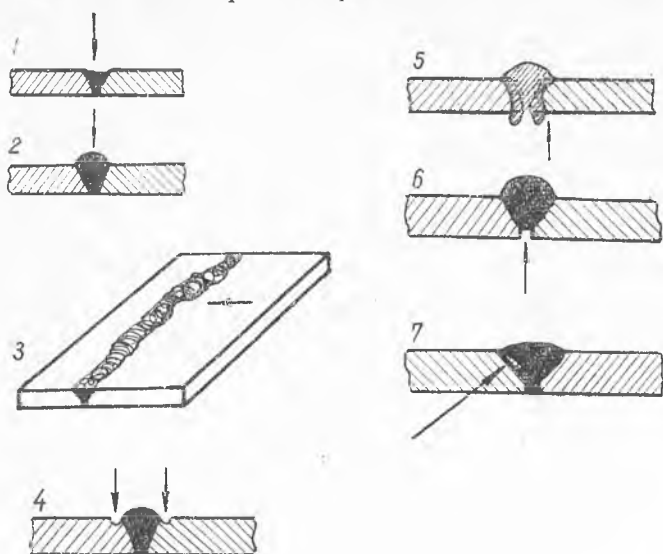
Некоторые дефекты сварных швов: 1 — ослабленный шов; 2 — чрезмерное усиление шва; 3 — неравномерная высота усиления и ширина шва; 4 — подрезы; 5 — прожоги; 6 — непровар по сечению; 7 — непровар по кромке
